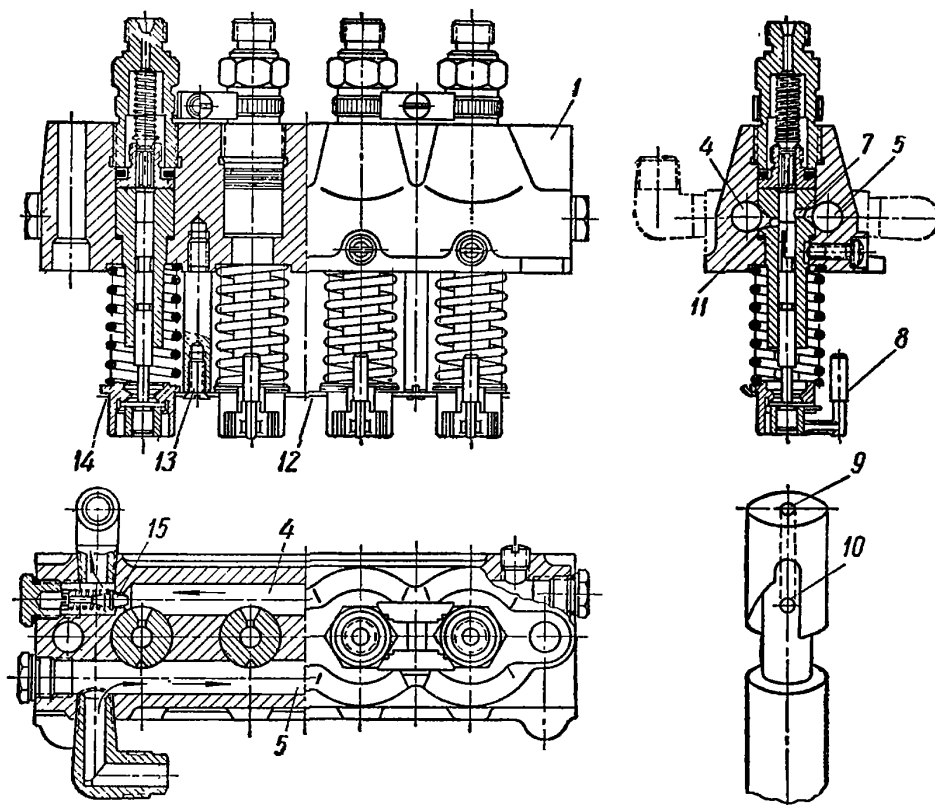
Топливный золотниковый насос двигателя Д-35.
